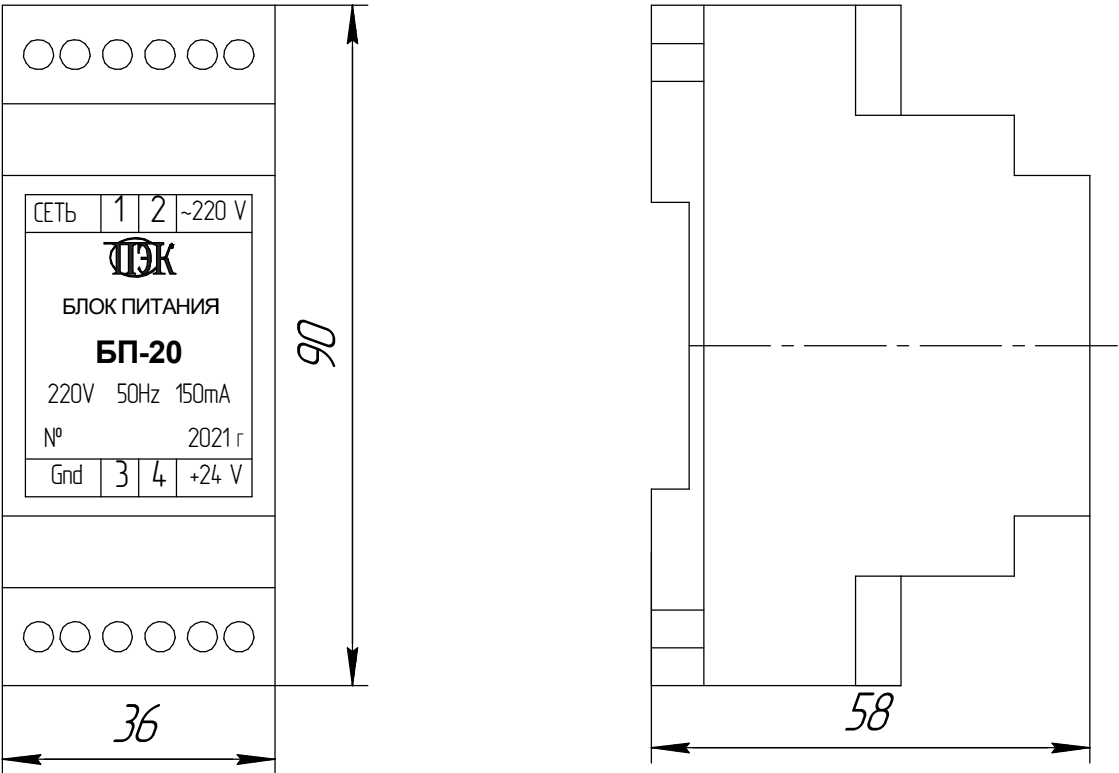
Габаритные размеры блока БП-20 (на DIN-рейке)
